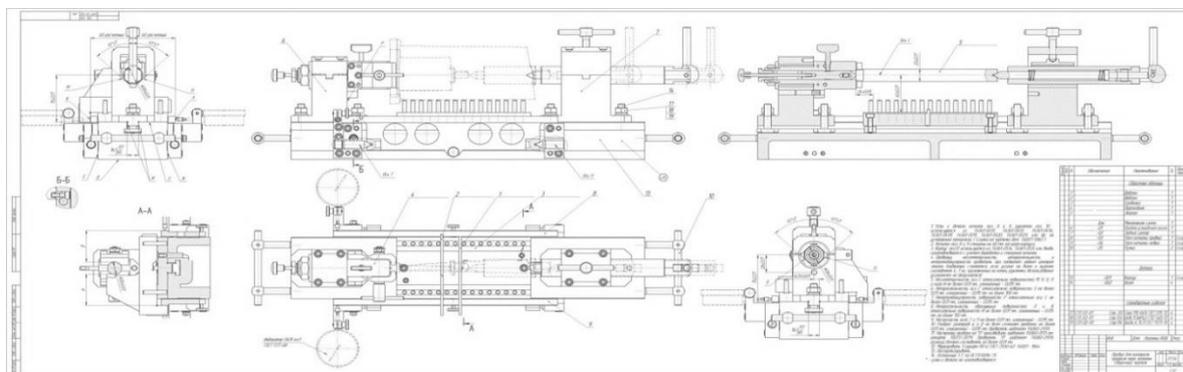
Прибор для контроля профиля пера лопаток КНД
